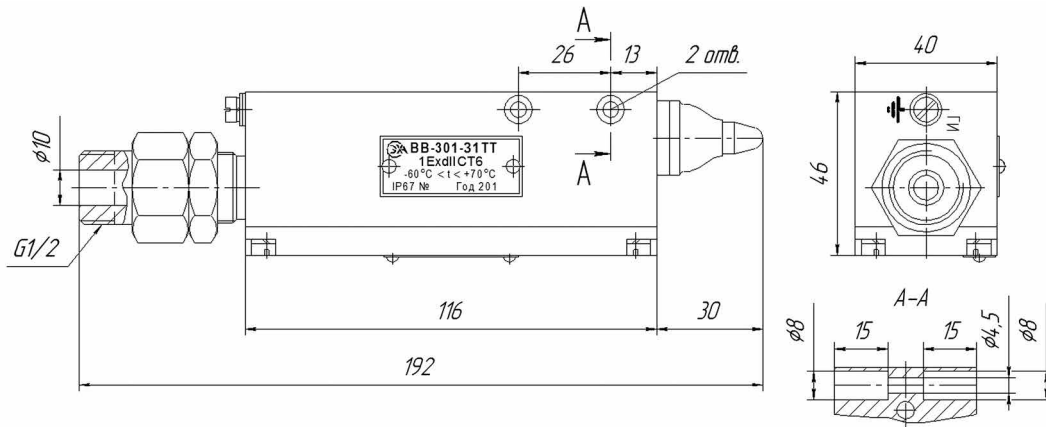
Габаритные и установочные размеры ВВ-301-31ТТ
